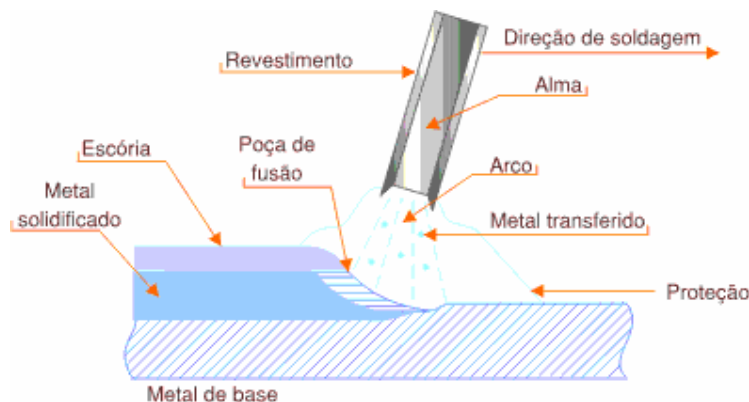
Soldagem com eletrodo revestido (Soares, 2007)
